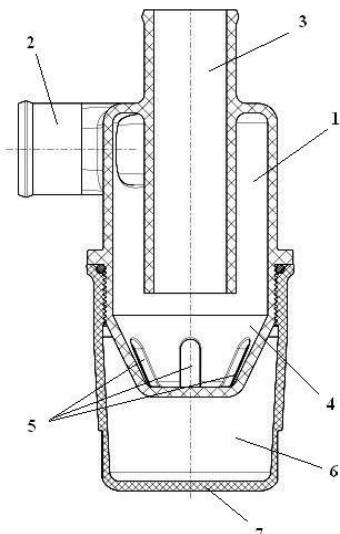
Конструктивная схема разработанного гидроциклонного фильтра-сепаратора (пластиковый вариант): 1 – цилиндрический корпус; 2 и 3 – входной и выходной патрубки; 4 – вихревая камера; 5 – улавливающие отверстия; 6 – грязесборник; 7 – корпус грязесборника
